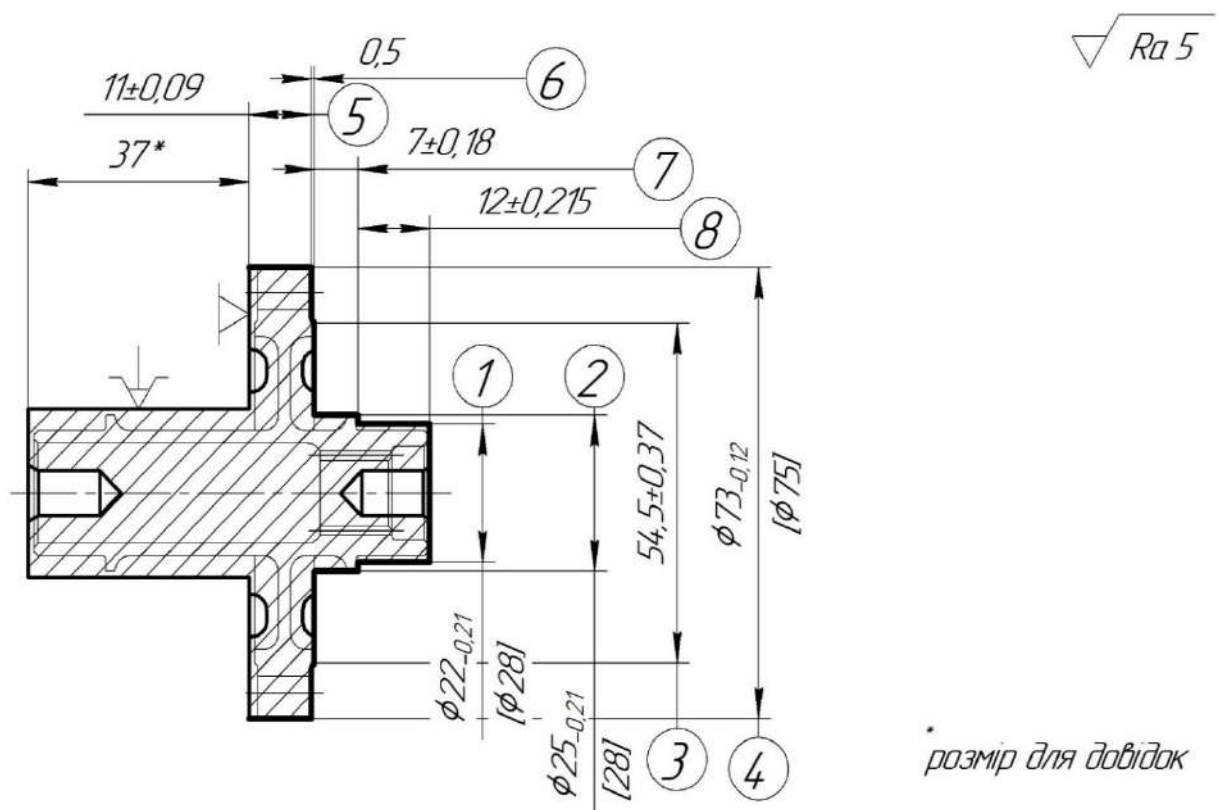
Ескиз операції №025 Токарна з ЧПК
